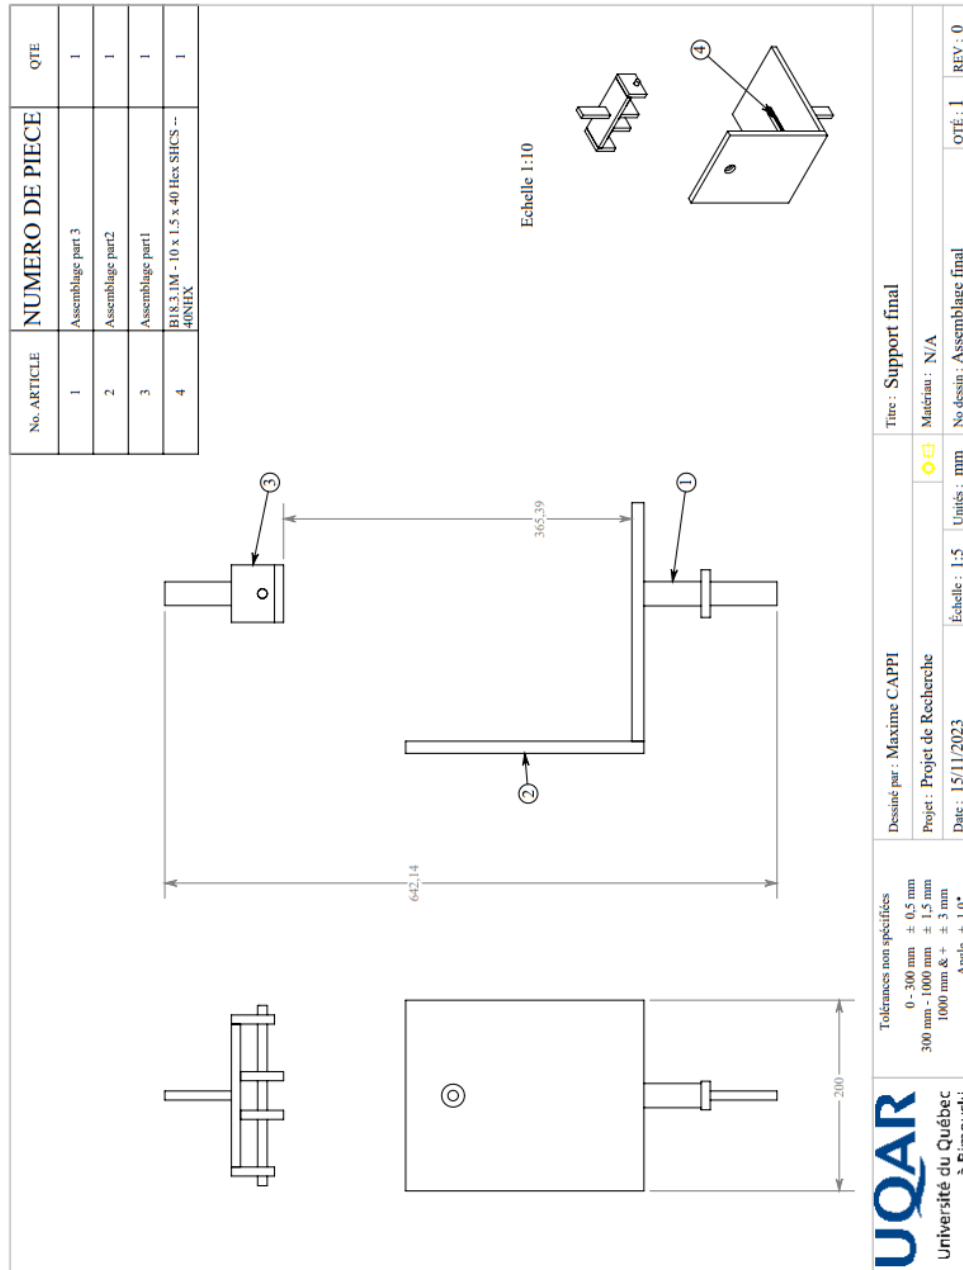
Plan d'assemblage du système d'accroche des prises d'escalades pour test de limite de rupture
